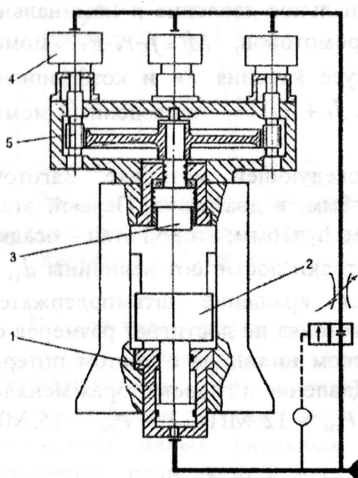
Конструктивная схема гидравлического пресса с гидромоторами на станине: 1 – цилиндр; 2 – ползун; 3 – штамподержатель; 4 – гидромоторы; 5 – зубчатая передача
